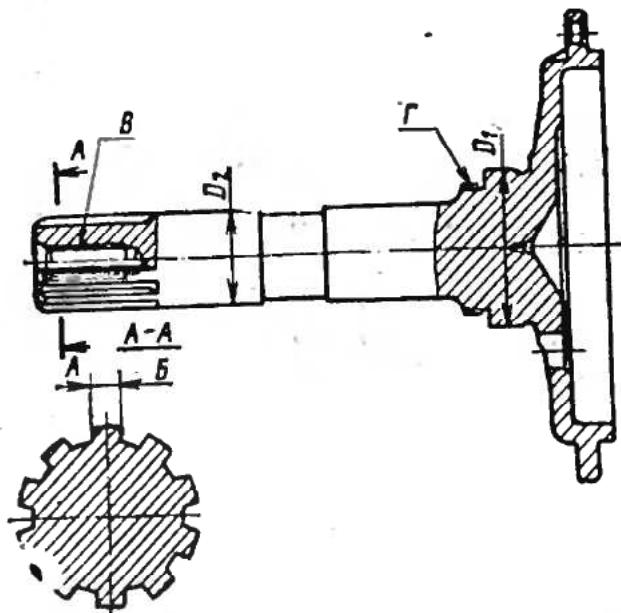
Вал ведомой шестерни редуктора переднего моста
